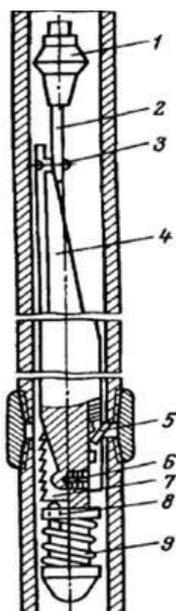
Схема отклонителя висячего типа, устанавливаемого на стыке труб: 1 – райбер; 2 – направление; 3 – болт; 4 – отклонитель; 5 – защелка; 6 – фиксатор; 7 – плашка; 8 – шток; 9 – пружина
